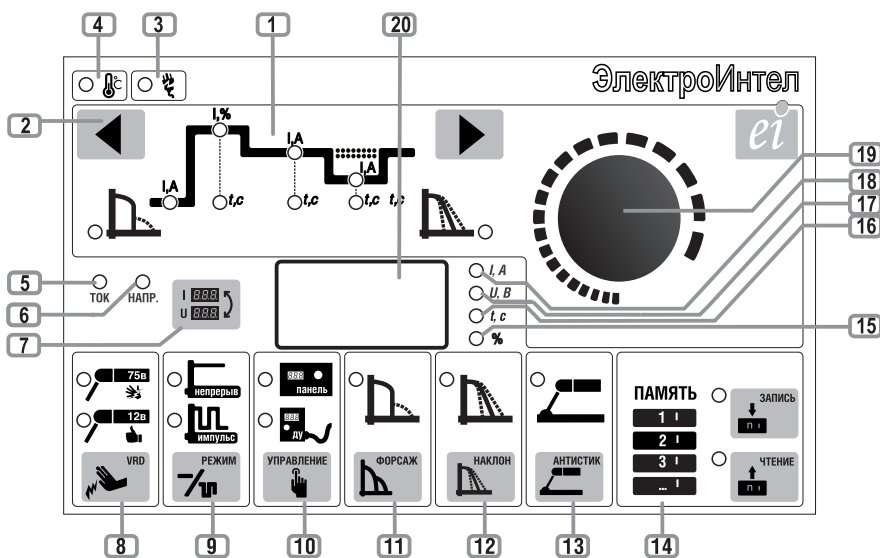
ВД-603. ВНЕШНИЙ ВИД
